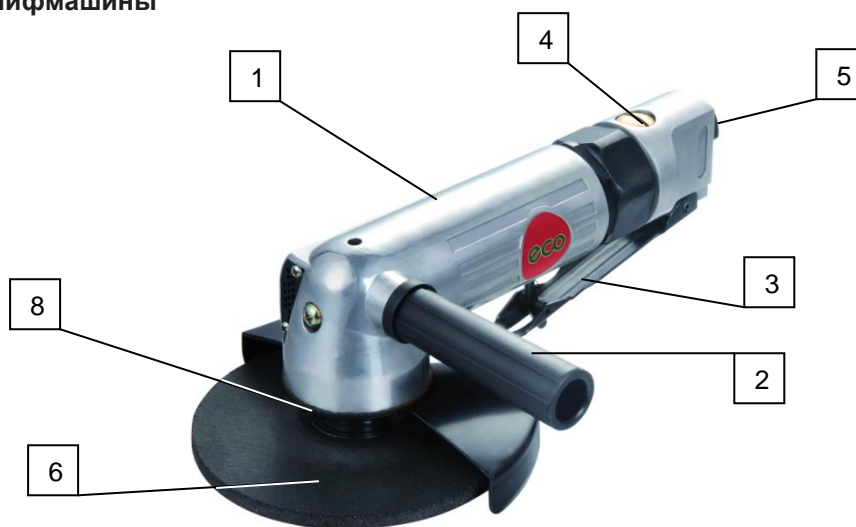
1. Корпус; 2. Рукоятка; 3. Выключатель; 4. Регулятор подачи сжатого воздуха; 5. Ниппель входной; 6. Отрезной круг; 7. Гайка прижимная (не представлена на рисунке); 8 Патрон.
